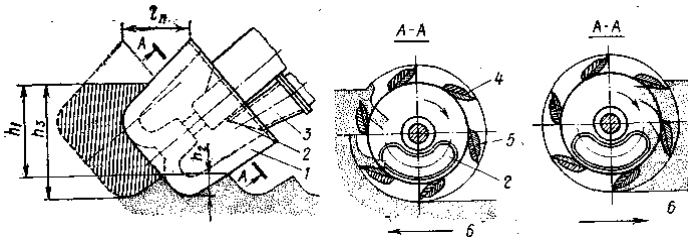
Схема фрезерного розпушувача: 1 - фреза; 2 - всмоктуючий отвір; 3 - всмоктуюча труба; 4 - ножі; 5 - ребра маточини; 6 - напрям переміщення фрези.
